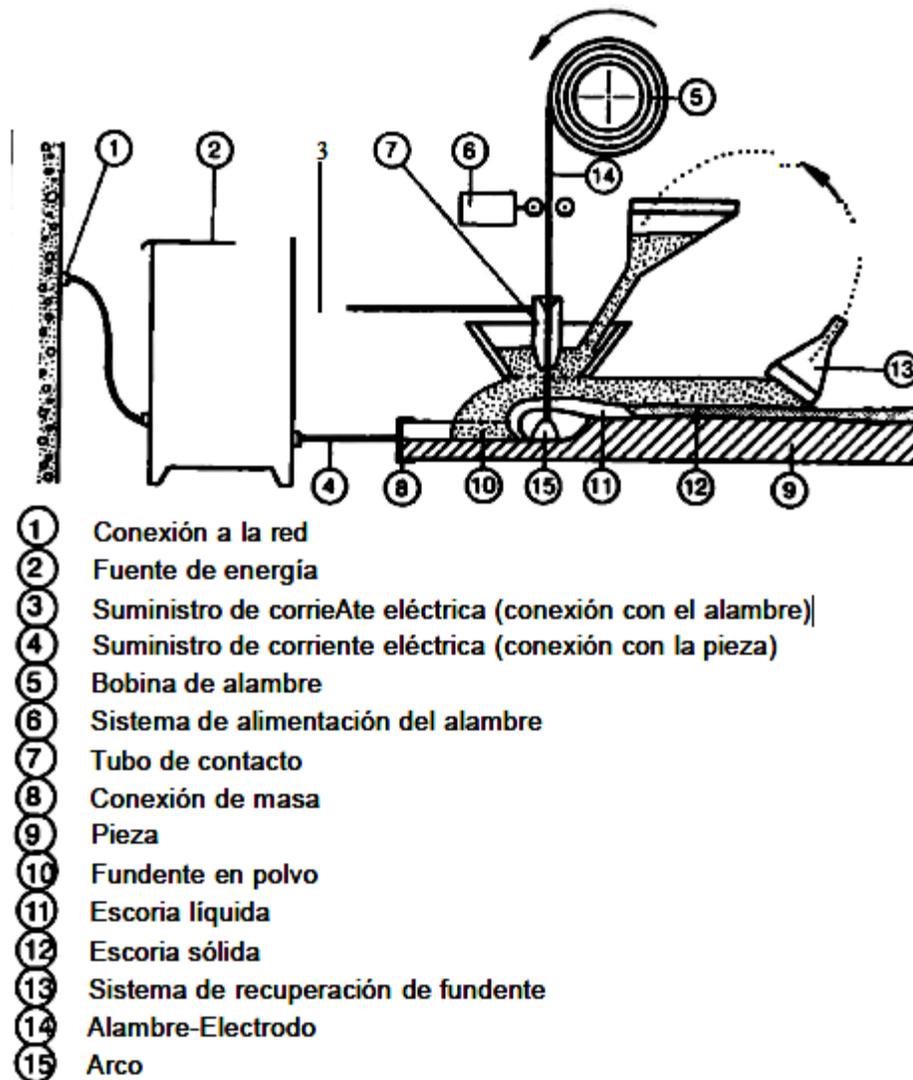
Equipo de soldadura por arco sumergido.
